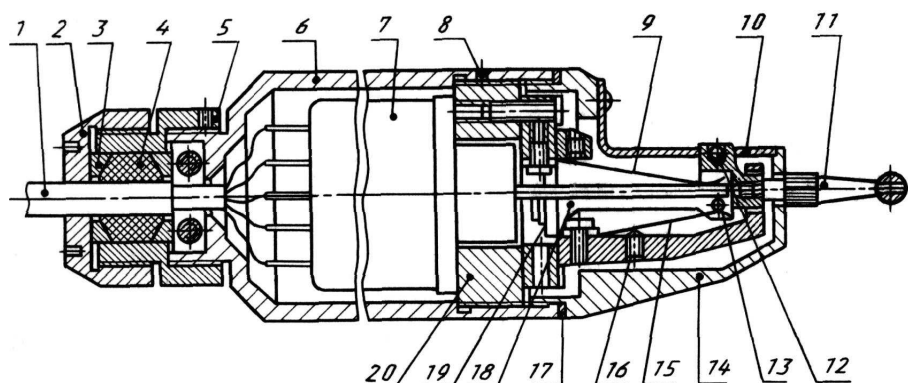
Устройство преобразователя с механотроном 6MX1С
